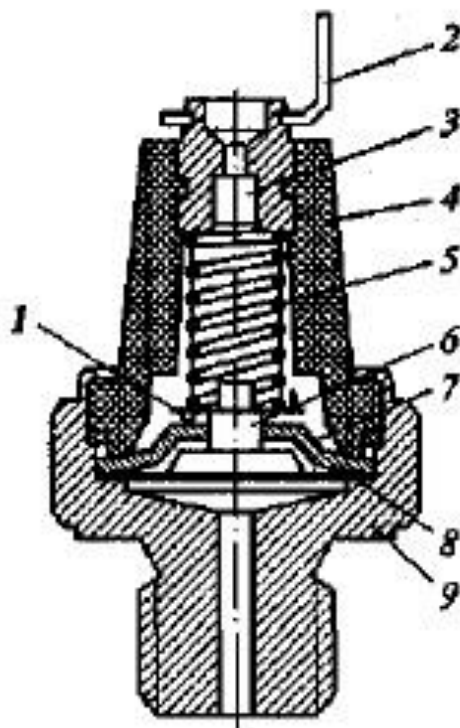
Датчик аварийного давления: 1 и 7 – контакты (подвижный и неподвижный); 2 – контактный разъем; 3 – фильтр; 4 – изолятор; 5 – пружина; 6 – толкатель; 8 – мембрана; 9 – корпус
